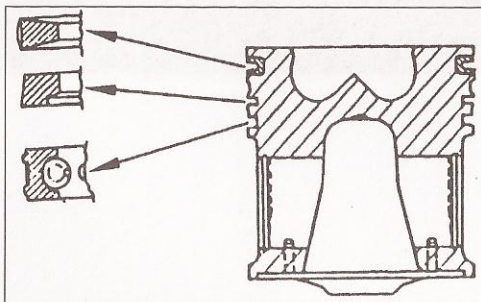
Расположение поршневых колец на поршне (двигатели 8040.45 и 8060.45)
